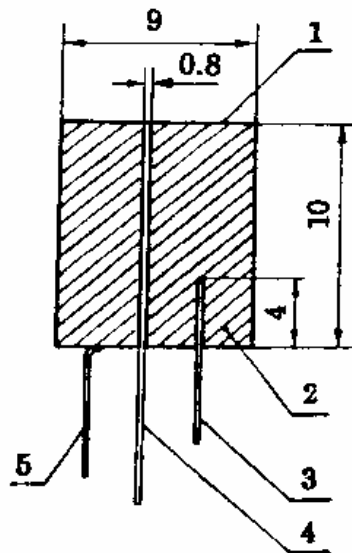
Sensor de termopar, dimensões em mm (LI et al., 1993)
